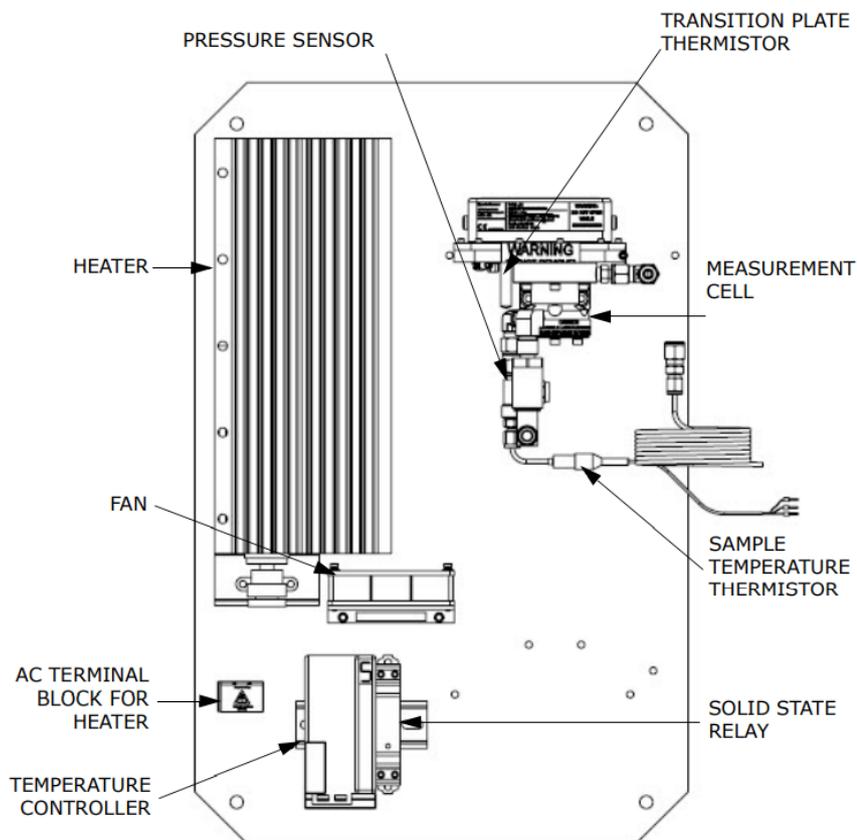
Componentes del conjunto del panel de la celda de muestra (celda de muestra de 0,1 m) (nivel inferior)
